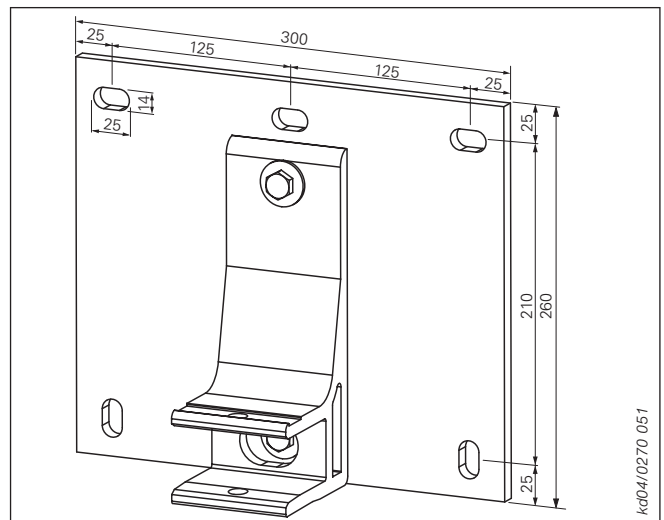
Consola tipo D – Fijación mural con placa de montaje grande 630/650/730/740/750
